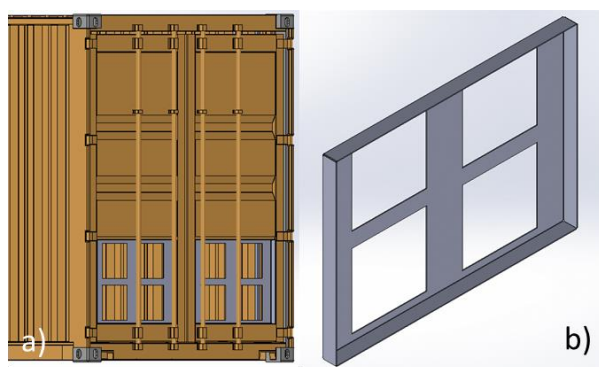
Modificaciones a portones del contenedor. En figura: a) vista general de ensamblaje de marcos soldados; b) vista en isométrico del marco para filtros.
